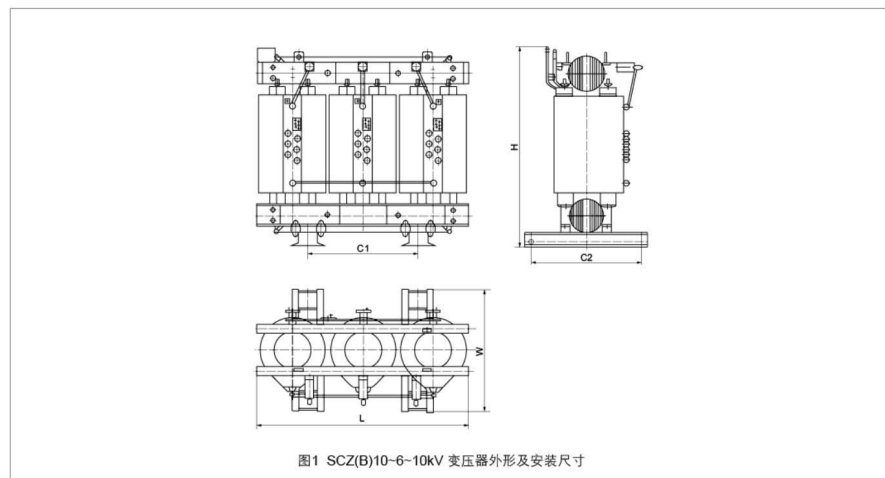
SCZ(B)10-6-10kV 变压器外形及安装尺寸
